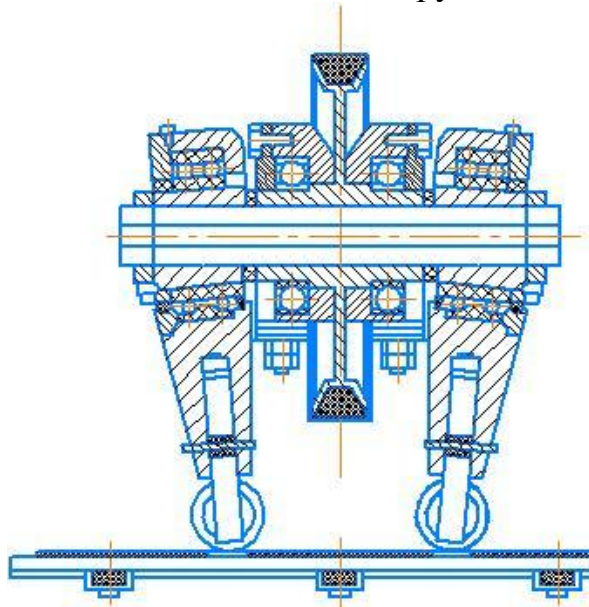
Привод ножей от механизма «Качающаяся шайба»
